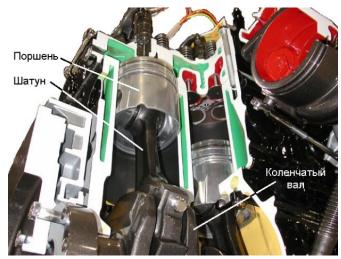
Частичный разрез двигателя, на котором виден: поршень *(piston)*, шатун *(connecting rod)* и коленчатый вал *(crankshaft)* двигателя.
